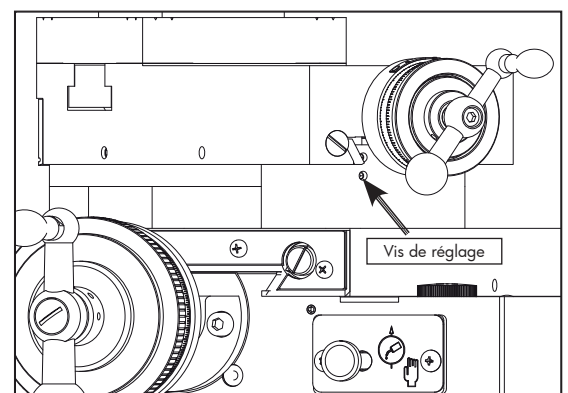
Vis de réglage du jeu du chariot porte-outil
